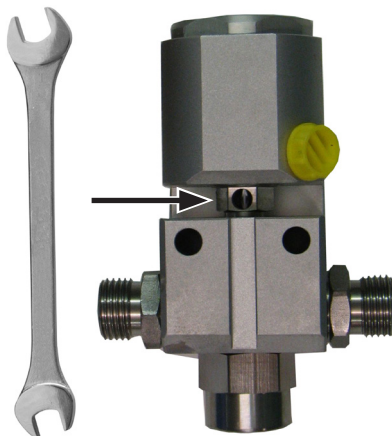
Packungsschraube mit Gabelschlüssel SW13 anziehen
